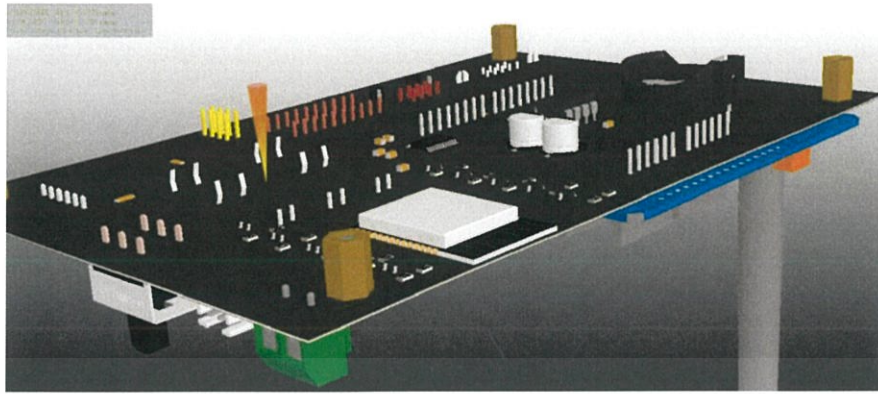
อุปกรณ์ต้นแบบบนแผ่น PCB อเนกประสงค์
